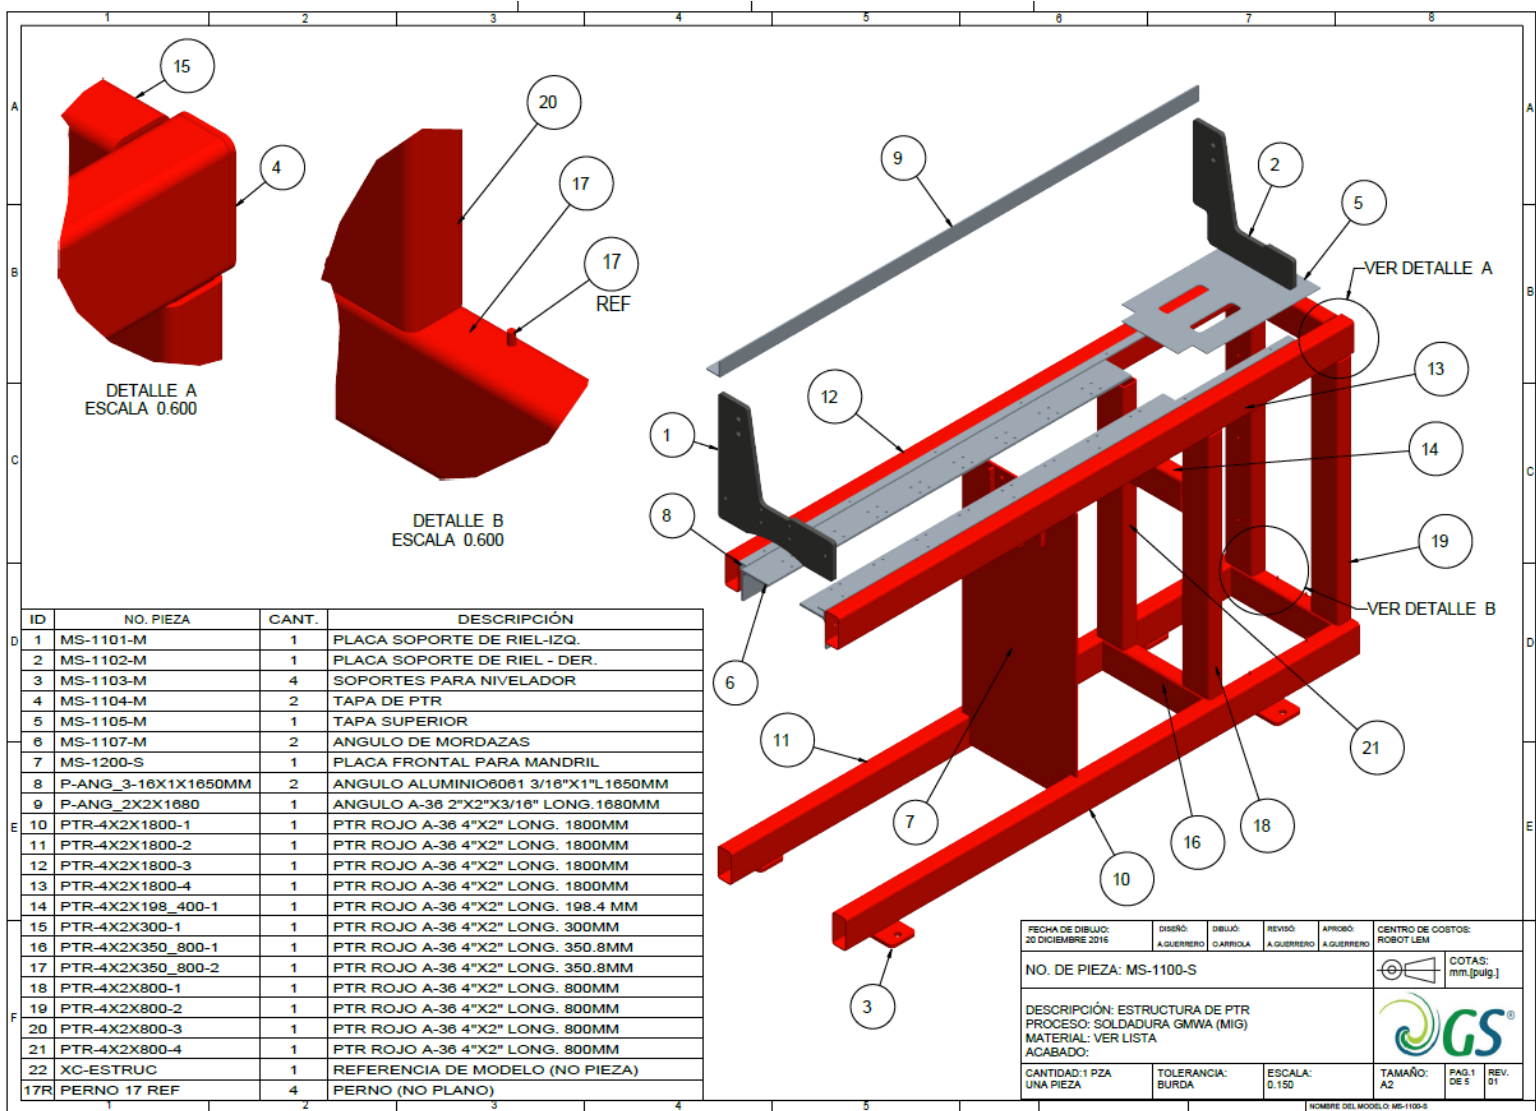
Base soporte para el sistema de soldadura para ductos de lámina (Cortesía Green Spare)
